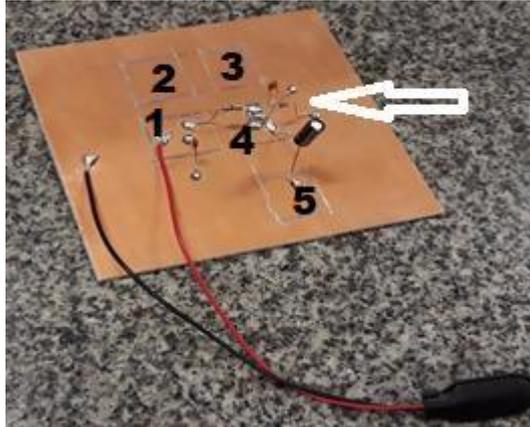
Soldagem do capacitor polarizado de 1 μ F
